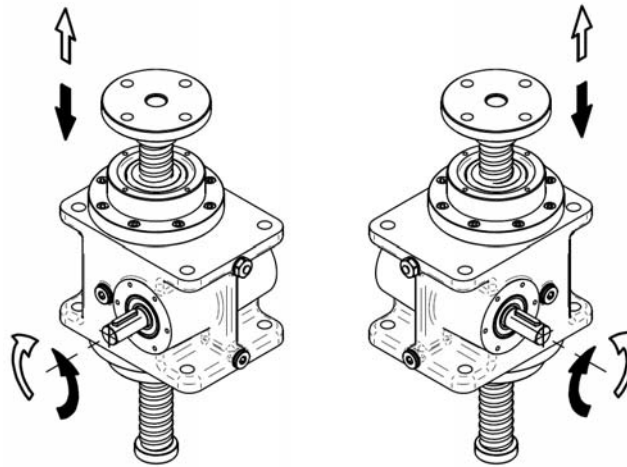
Hubrichtungen des Kugelgewinde-Hubgetriebes
